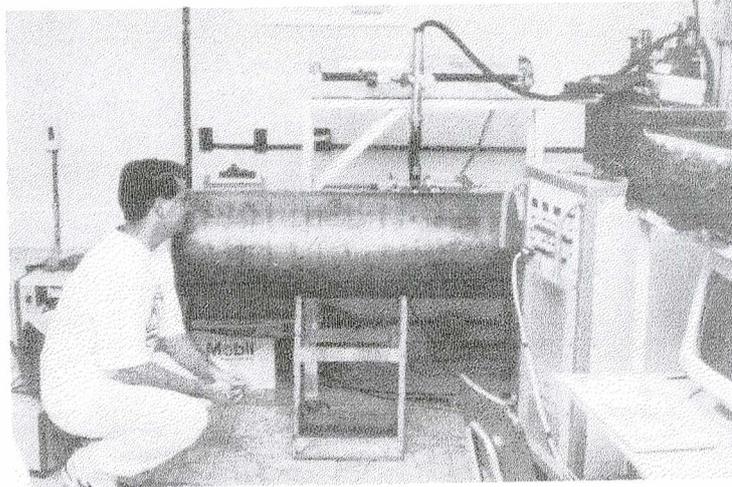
8 - Soldagem do cilindro do rolo-facas
